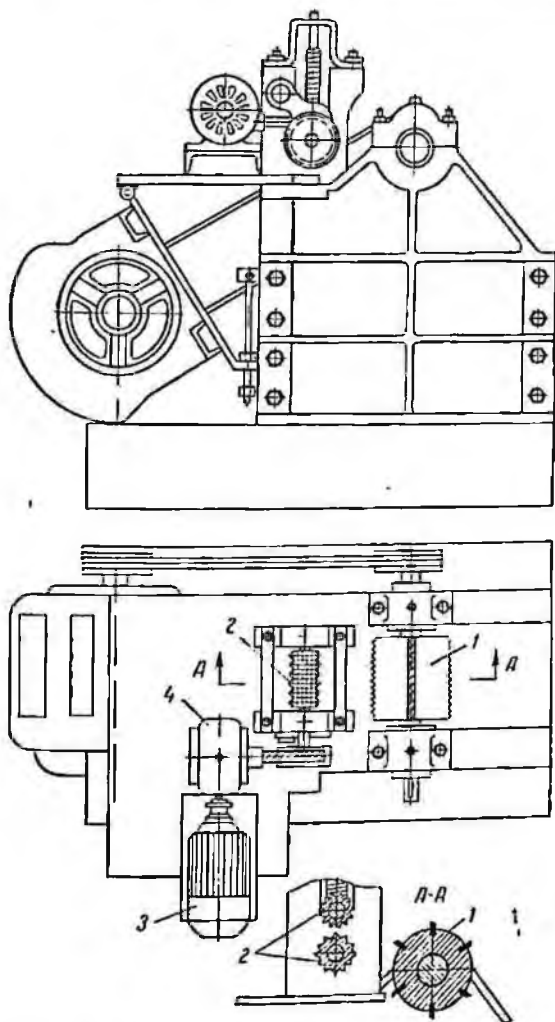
Станок для приготовления кордио-резинового наполнителя.
